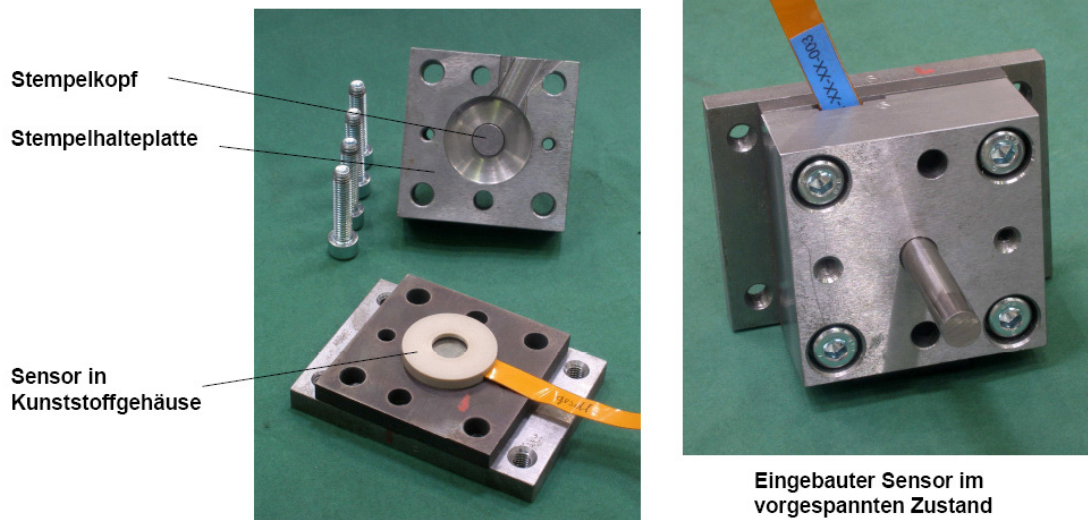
Plattensystem des Schneidwerkzeuges mit eingebaustem Sensor
